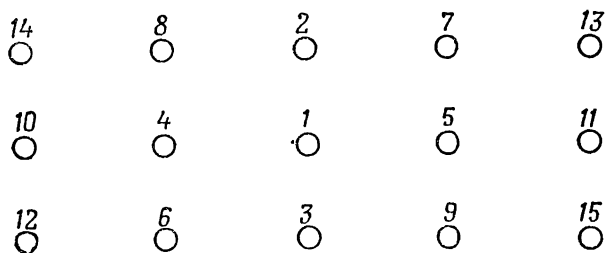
Схема последовательности затяжки болтов крепления головки блока цилиндров
